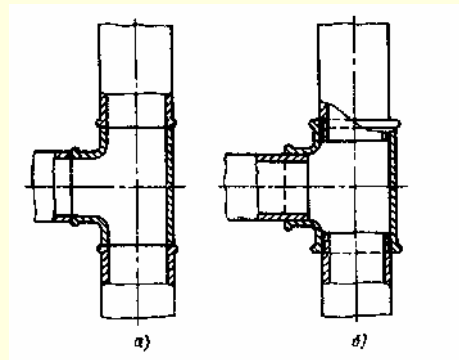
Схема кольцевого выступа в стандартном тройнике: а – сварной тройник; б – соединение труб в тройнике на резьбе
